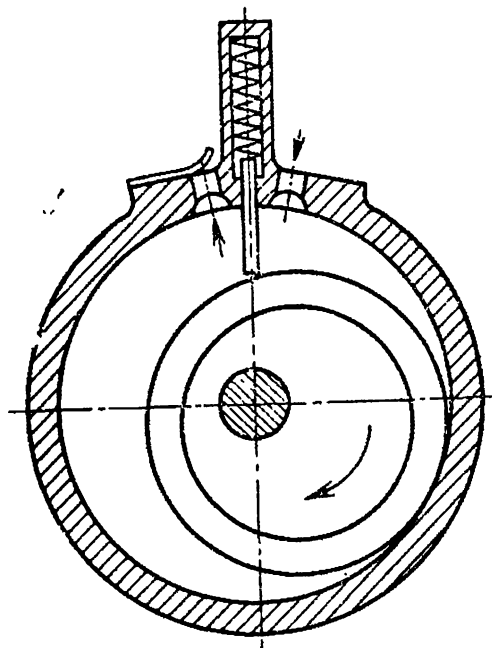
Схема компрессора с катящимся ротором и разделяющей пластиной, направляемой радиальной прорезью в цилиндре (пластина прижимается к ротору пружиной).
